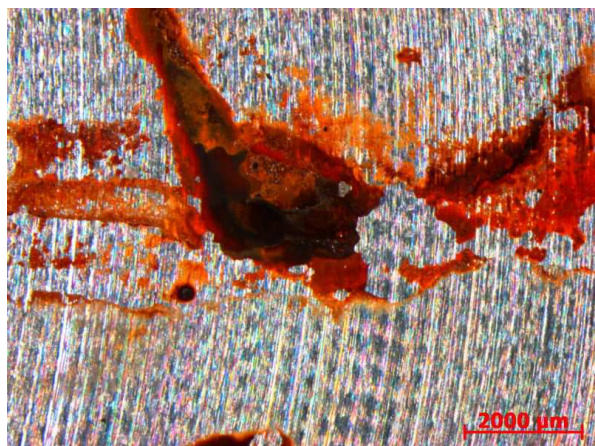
Makrosnímky laserových návarů Inconel 625 se zvýšeným obsahem molybdenu po Korozní zkoušce v solné mlze; Zkouška byla provedena dle ČSN EN ISO 9227; doba trvání zkoušky 240 h
